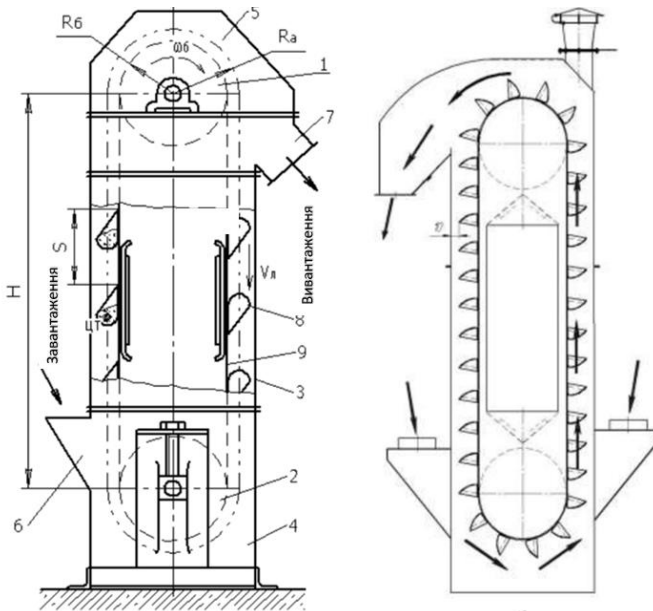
Конструкція норії: 1 – верхній (привідний) барабан; 2 – нижній (натяжний барабан); 3 – кожух; 4 - черевик норії; 5 – головка норії; 6 – завантажувальна горловина; 7 – вивантажувальна горловина; 8 – ківш; 9 – норійна стрічка.
